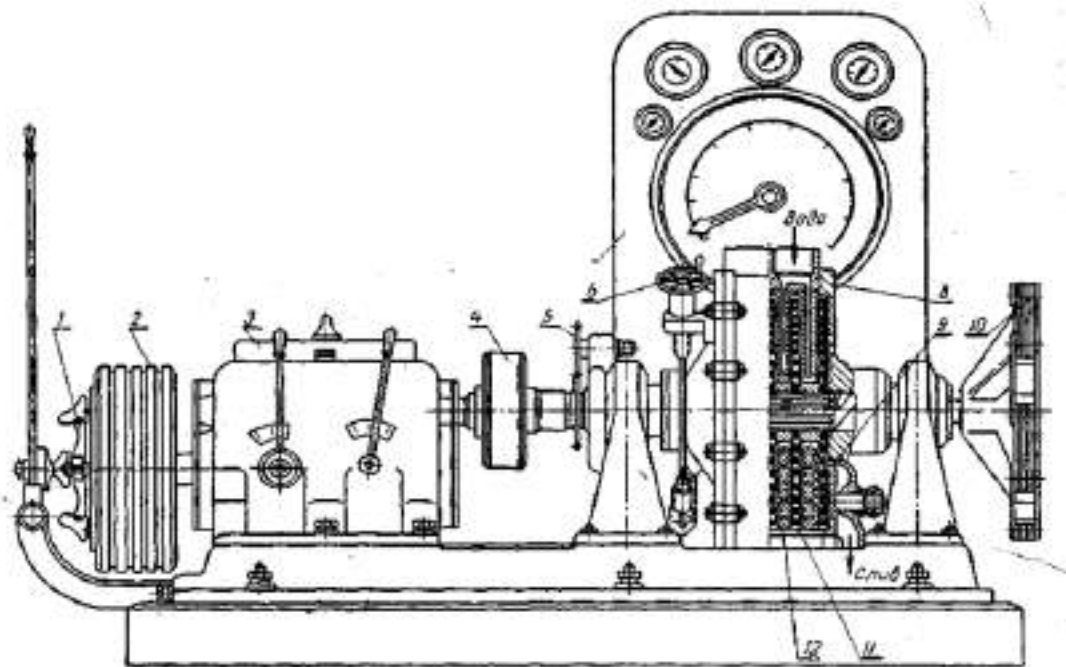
Обкатувально-гальмівний стенд ВІД-6 з гідрогальмом: 1 – муфта зчеплення; 2 – приводної. шків; 3 – редуктор; 4 – муфта вільного ходу; 5 – привод електротакметра; 6 – маховичок приводу регульовального клапана; 7 – щит вимірювальних приладів; 8 – корпус гідрогальма; 9 – регульовальні клапани (лівий і правий); 10 – сполучна муфта; 11 – сталевий перфорований диск ротора; 12 – нерухомий чавунний диск.
